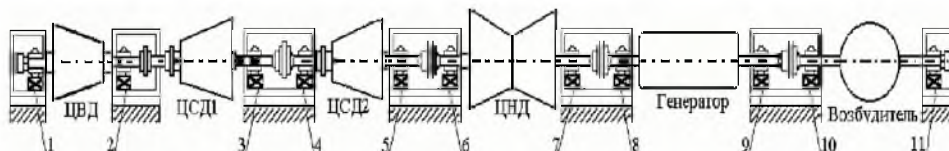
Схема объекта исследования (1–11 – номер опоры): ЦВД – цилиндр высокого давления; ЦСД – цилиндр среднего давления; ЦНД – цилиндр низкого давления.
